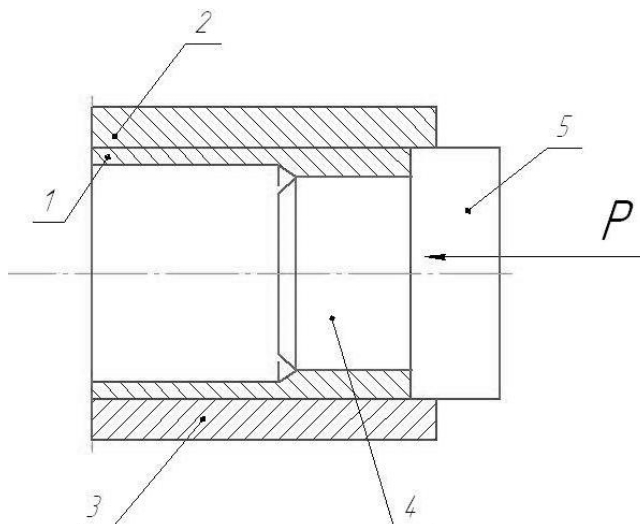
Схема локальной деформации полой заготовки с уменьшением ее внутреннего диаметра
